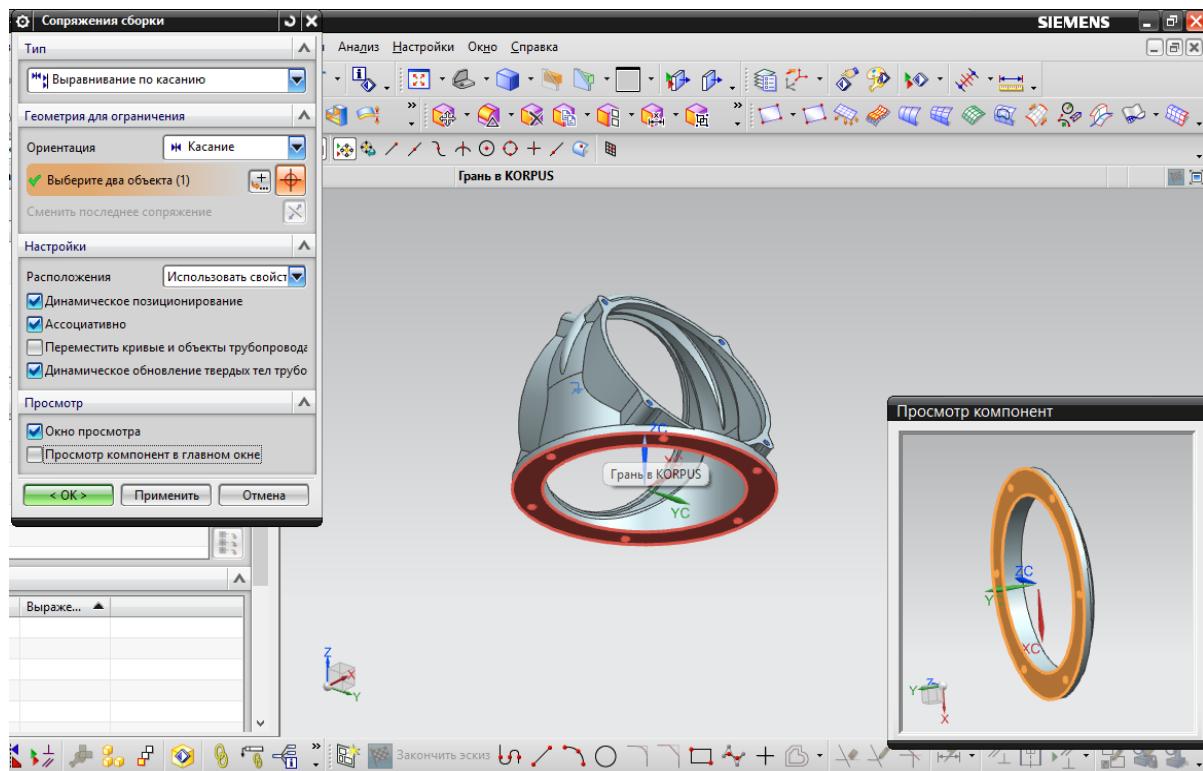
Выбор сопрягаемых поверхностей фланца и корпуса
